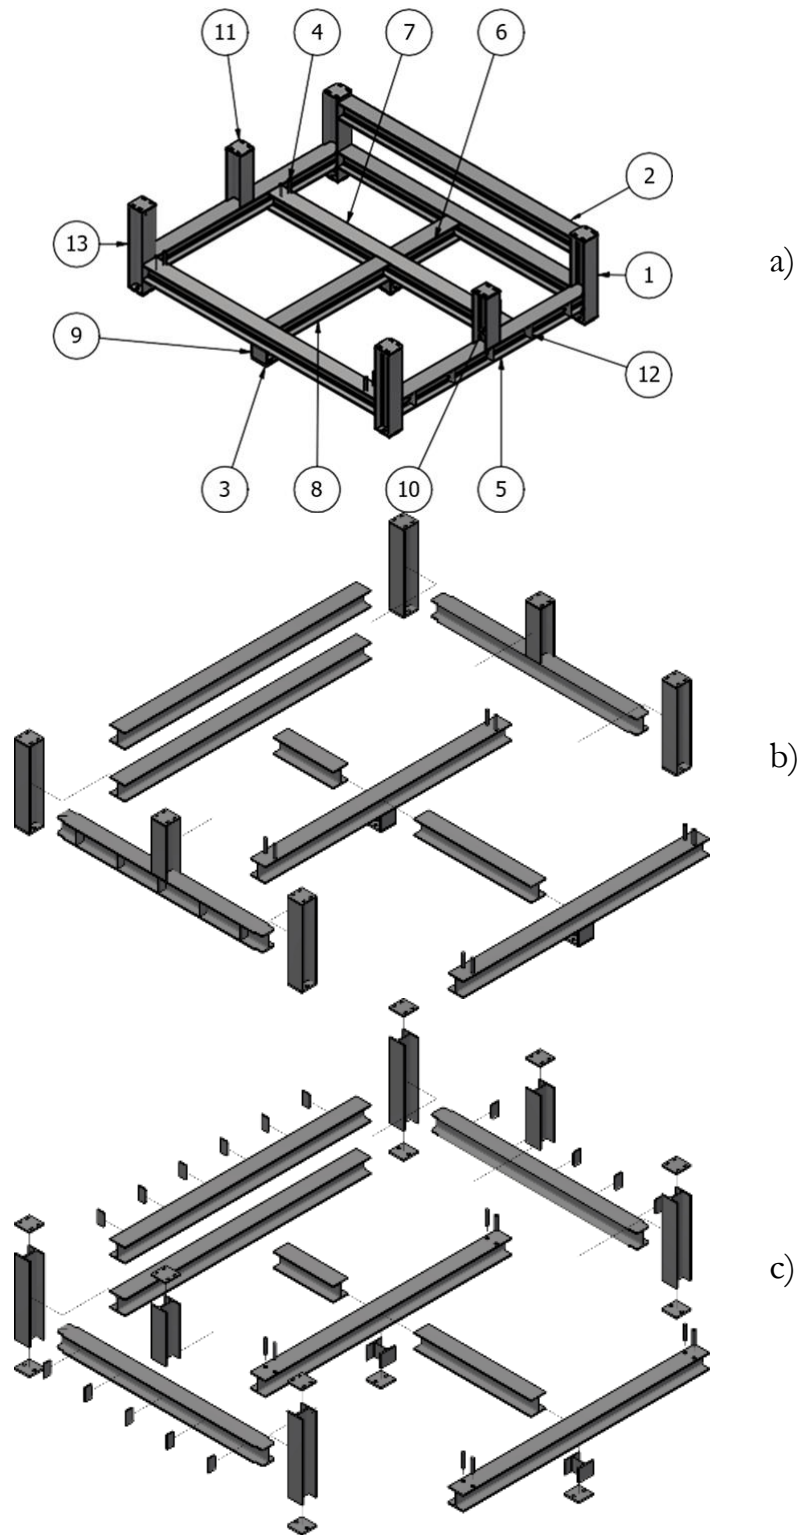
Estrutura soldada da base M&G_PMM_F_B:
